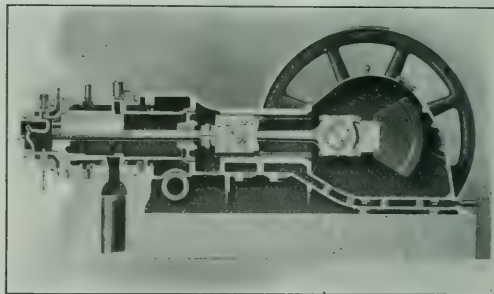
MOTOR SEMI-DIESEL BESSEMER
